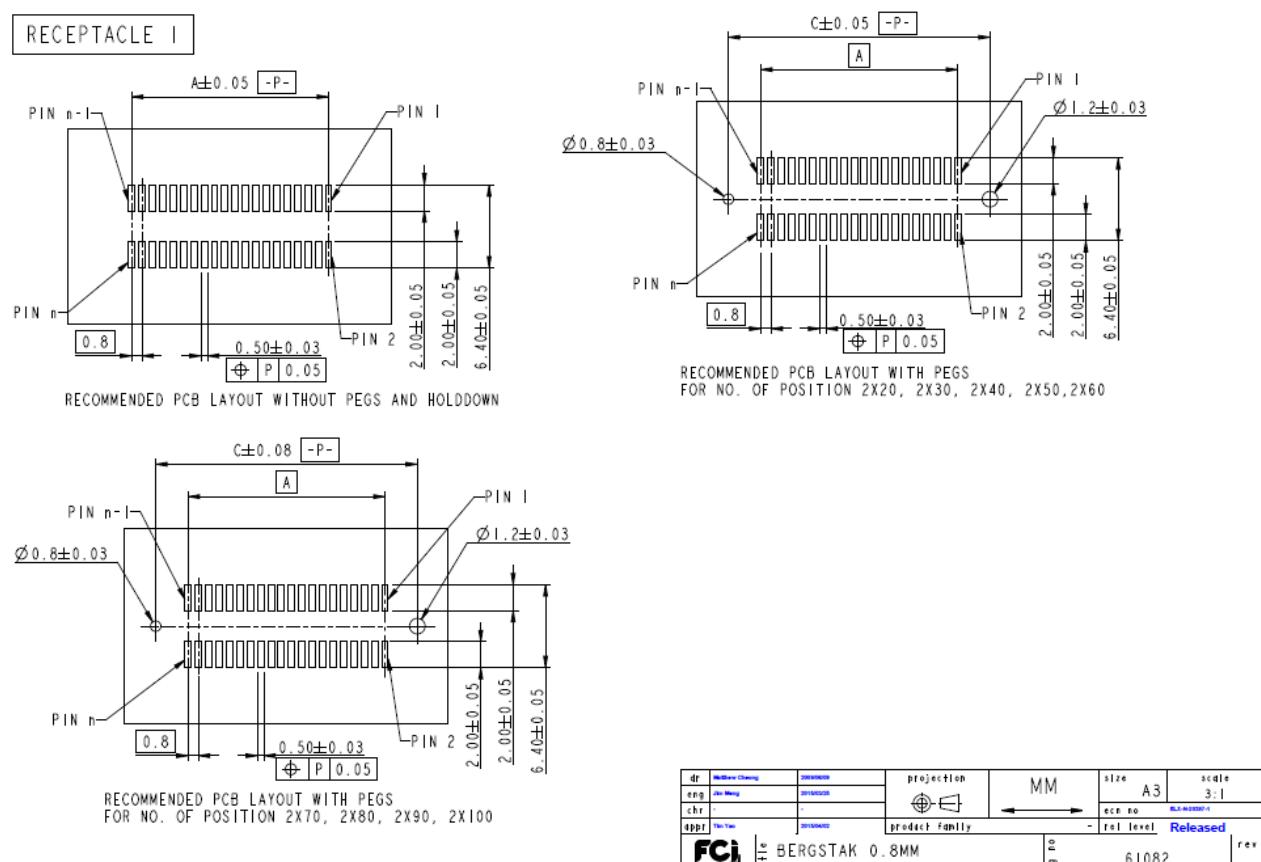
间距 0.8mm 立式双排 80 PIN PCB 封装
